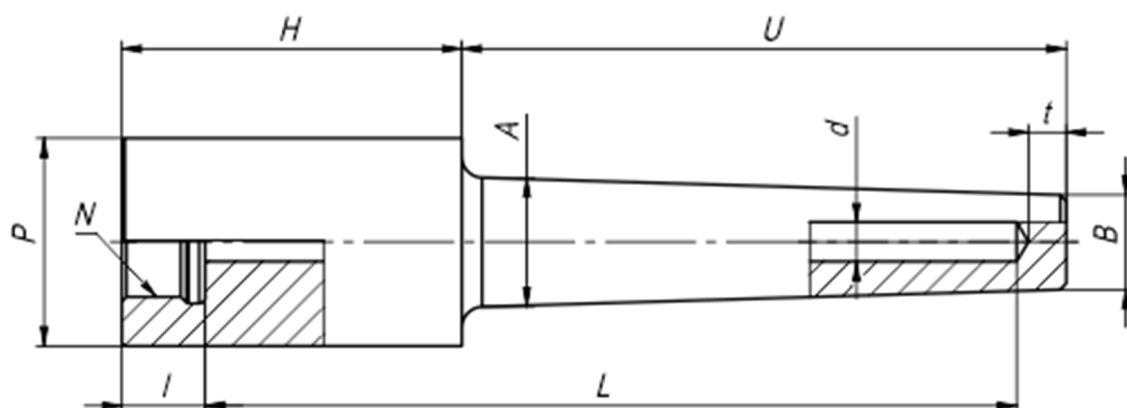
Гильза под приварку через адаптер (Socket Weld), цельноточёная, коническая, под подвижный штанцер.
